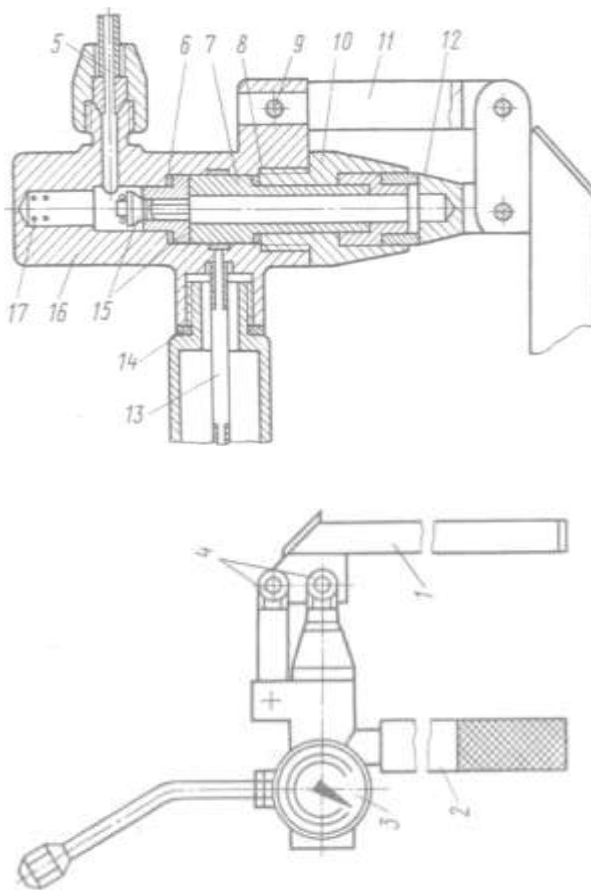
Приспособление для проверки форсунок и прецизионных пар топливного насоса КИ-16301А
